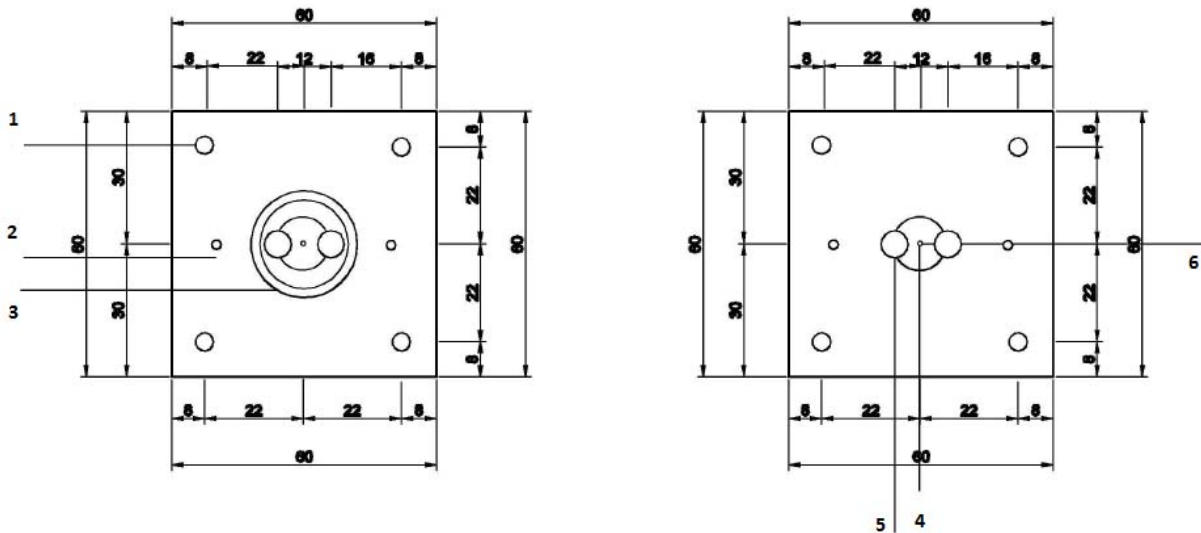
Grundriss der Konstruierten Zelle: 1 – Imbusschrauben; 2 – Dichtungsring; 3 – Führung; 4 – Platinelektrode; 5 – Inlett/Outlet für Elektrolyt, 6 – Elektrolyt Kammer, erstellt mit AutoCAD.
